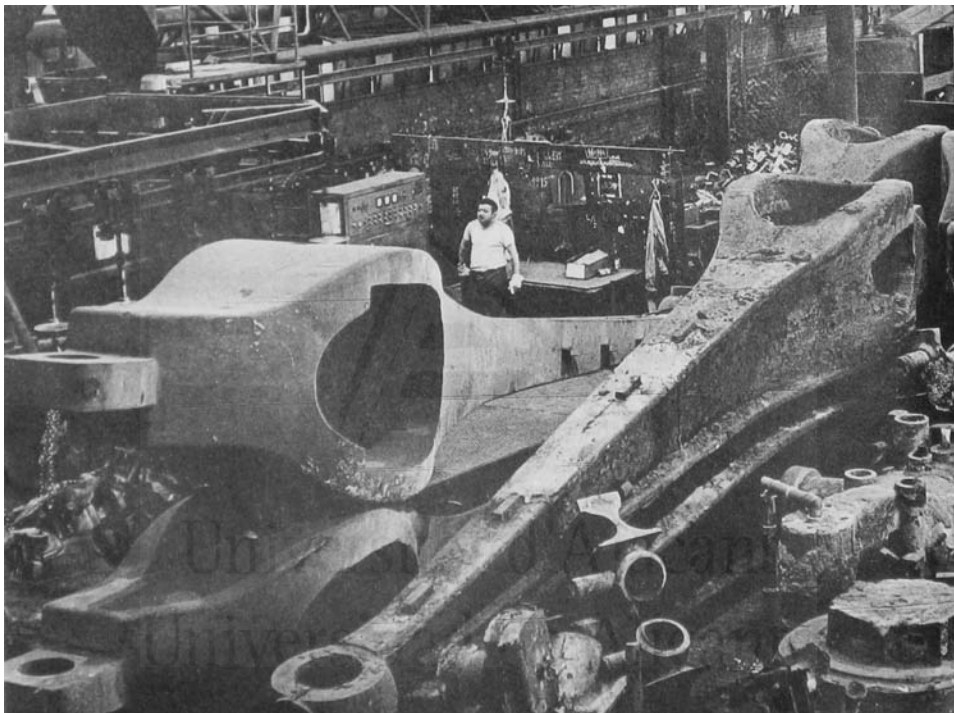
Vigas Gerber en la fundición. Ilustración extraída de "*Mémoires d'un ingénieur*" (Rice, 1998A, p.32).
